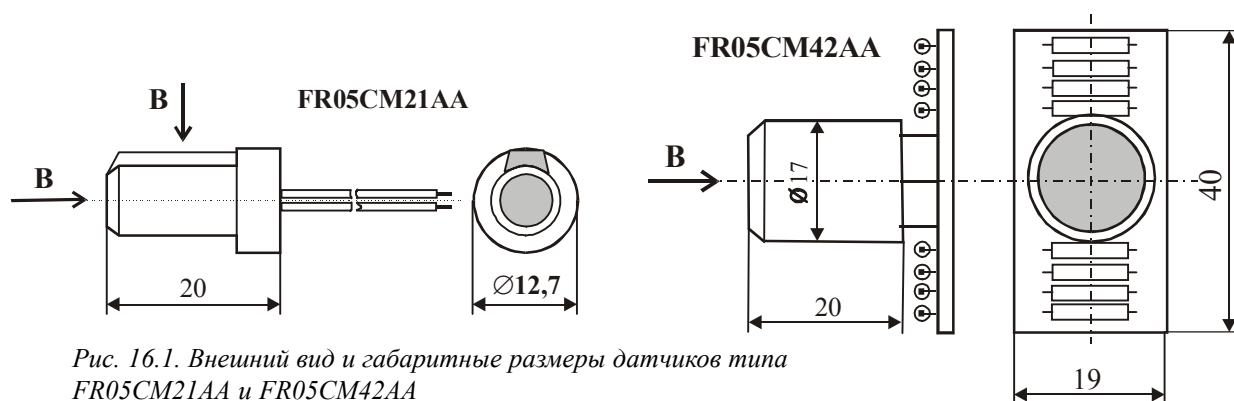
Внешний вид и габаритные размеры датчиков типа FR05CM21AA и FR05CM42AA
